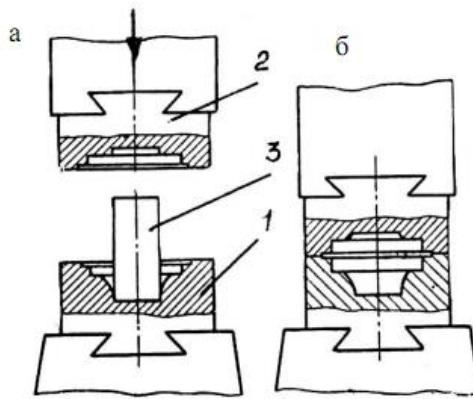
Одноручевой штамп для горячей штамповки
